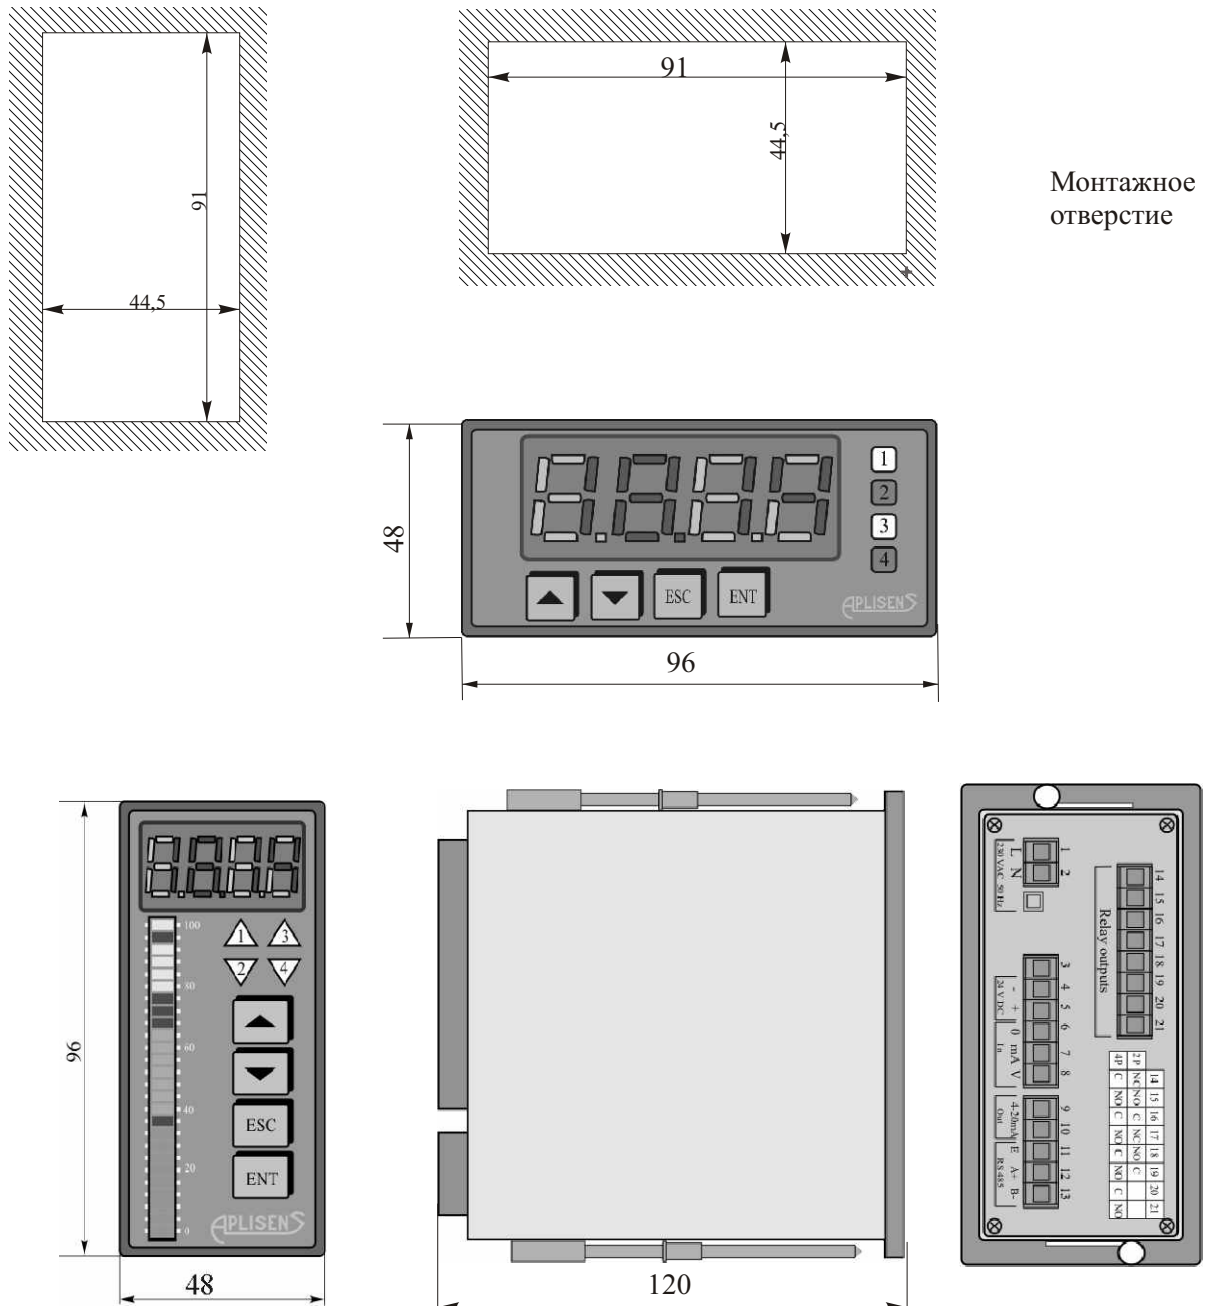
Внешний вид, габаритные и установочные размеры. Размеры монтажного отверстия
